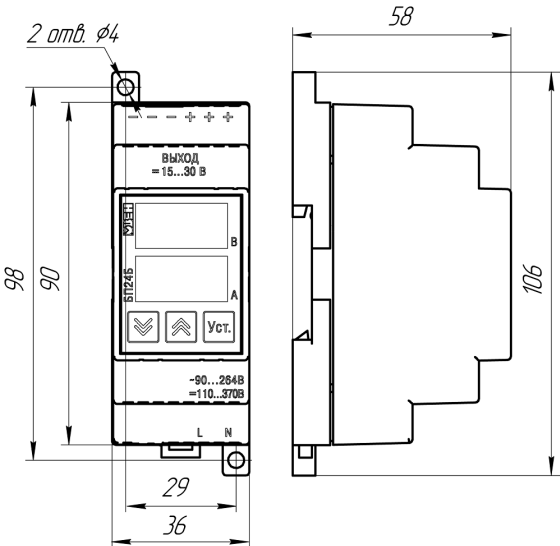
Внешний вид, габаритные и установочные размеры прибора
